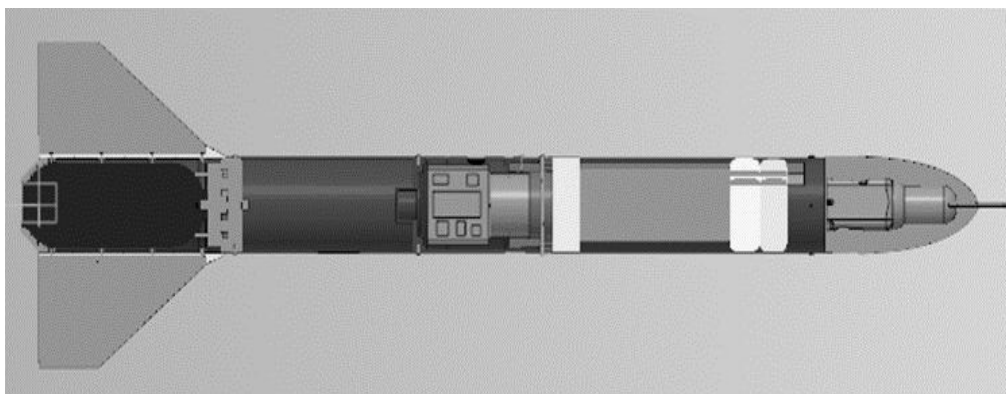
Ракета-носитель измерительного оборудования. Вид в разрезе
